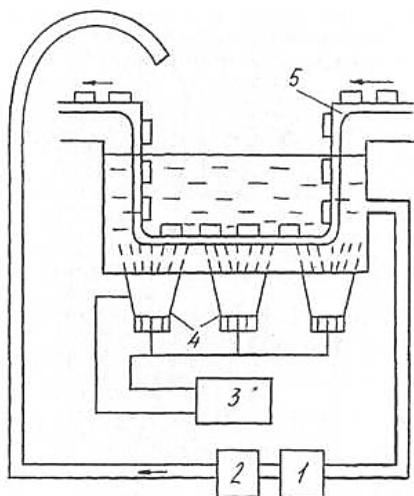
Схема ультразвуковой установки для очистки деталей:
